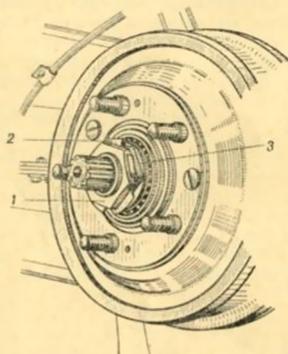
Регулировочный узел подшипников ступицы переднего колеса
